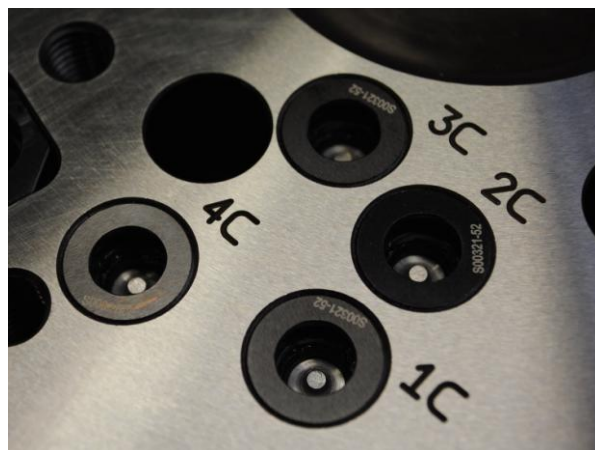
Vyrobené tělo univerzálního adaptéru
